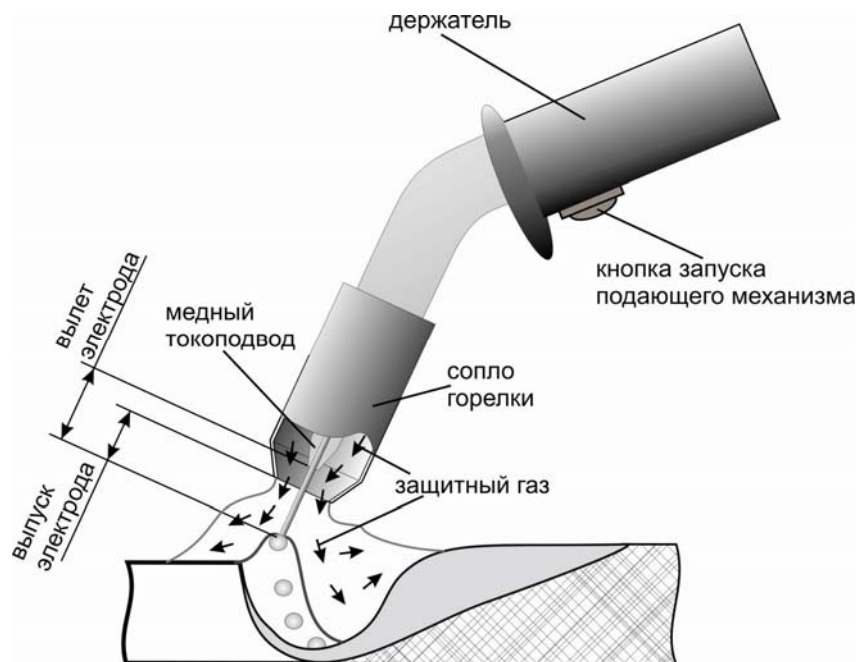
Схема процесса механизированной сварки в защитных газах
